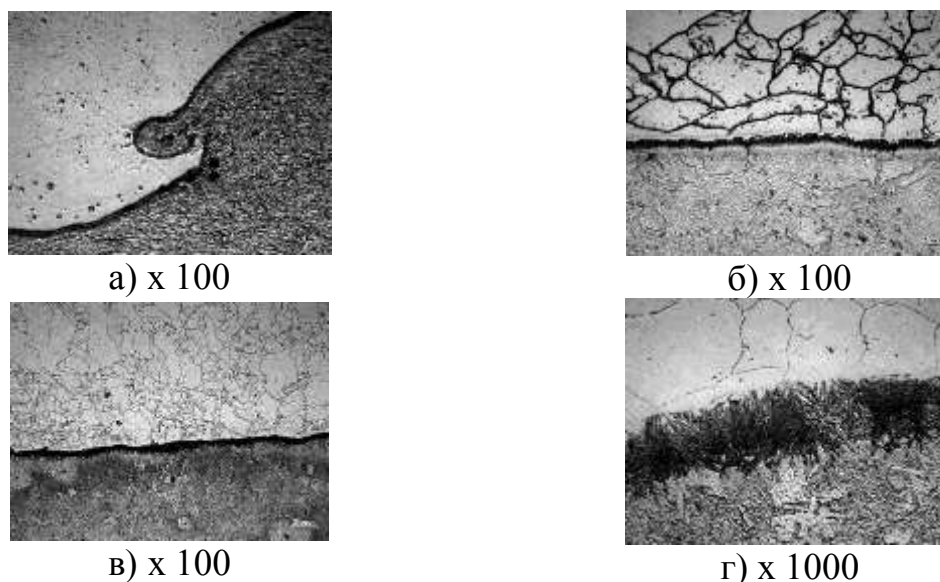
Строение границы сцепления плакированной стали АБ2-2 + 04Х20Н6Г11М2АФБ после: а) сварки взрывом, б) пакетной прокатки, в, г) электрошлаковой наплавки
